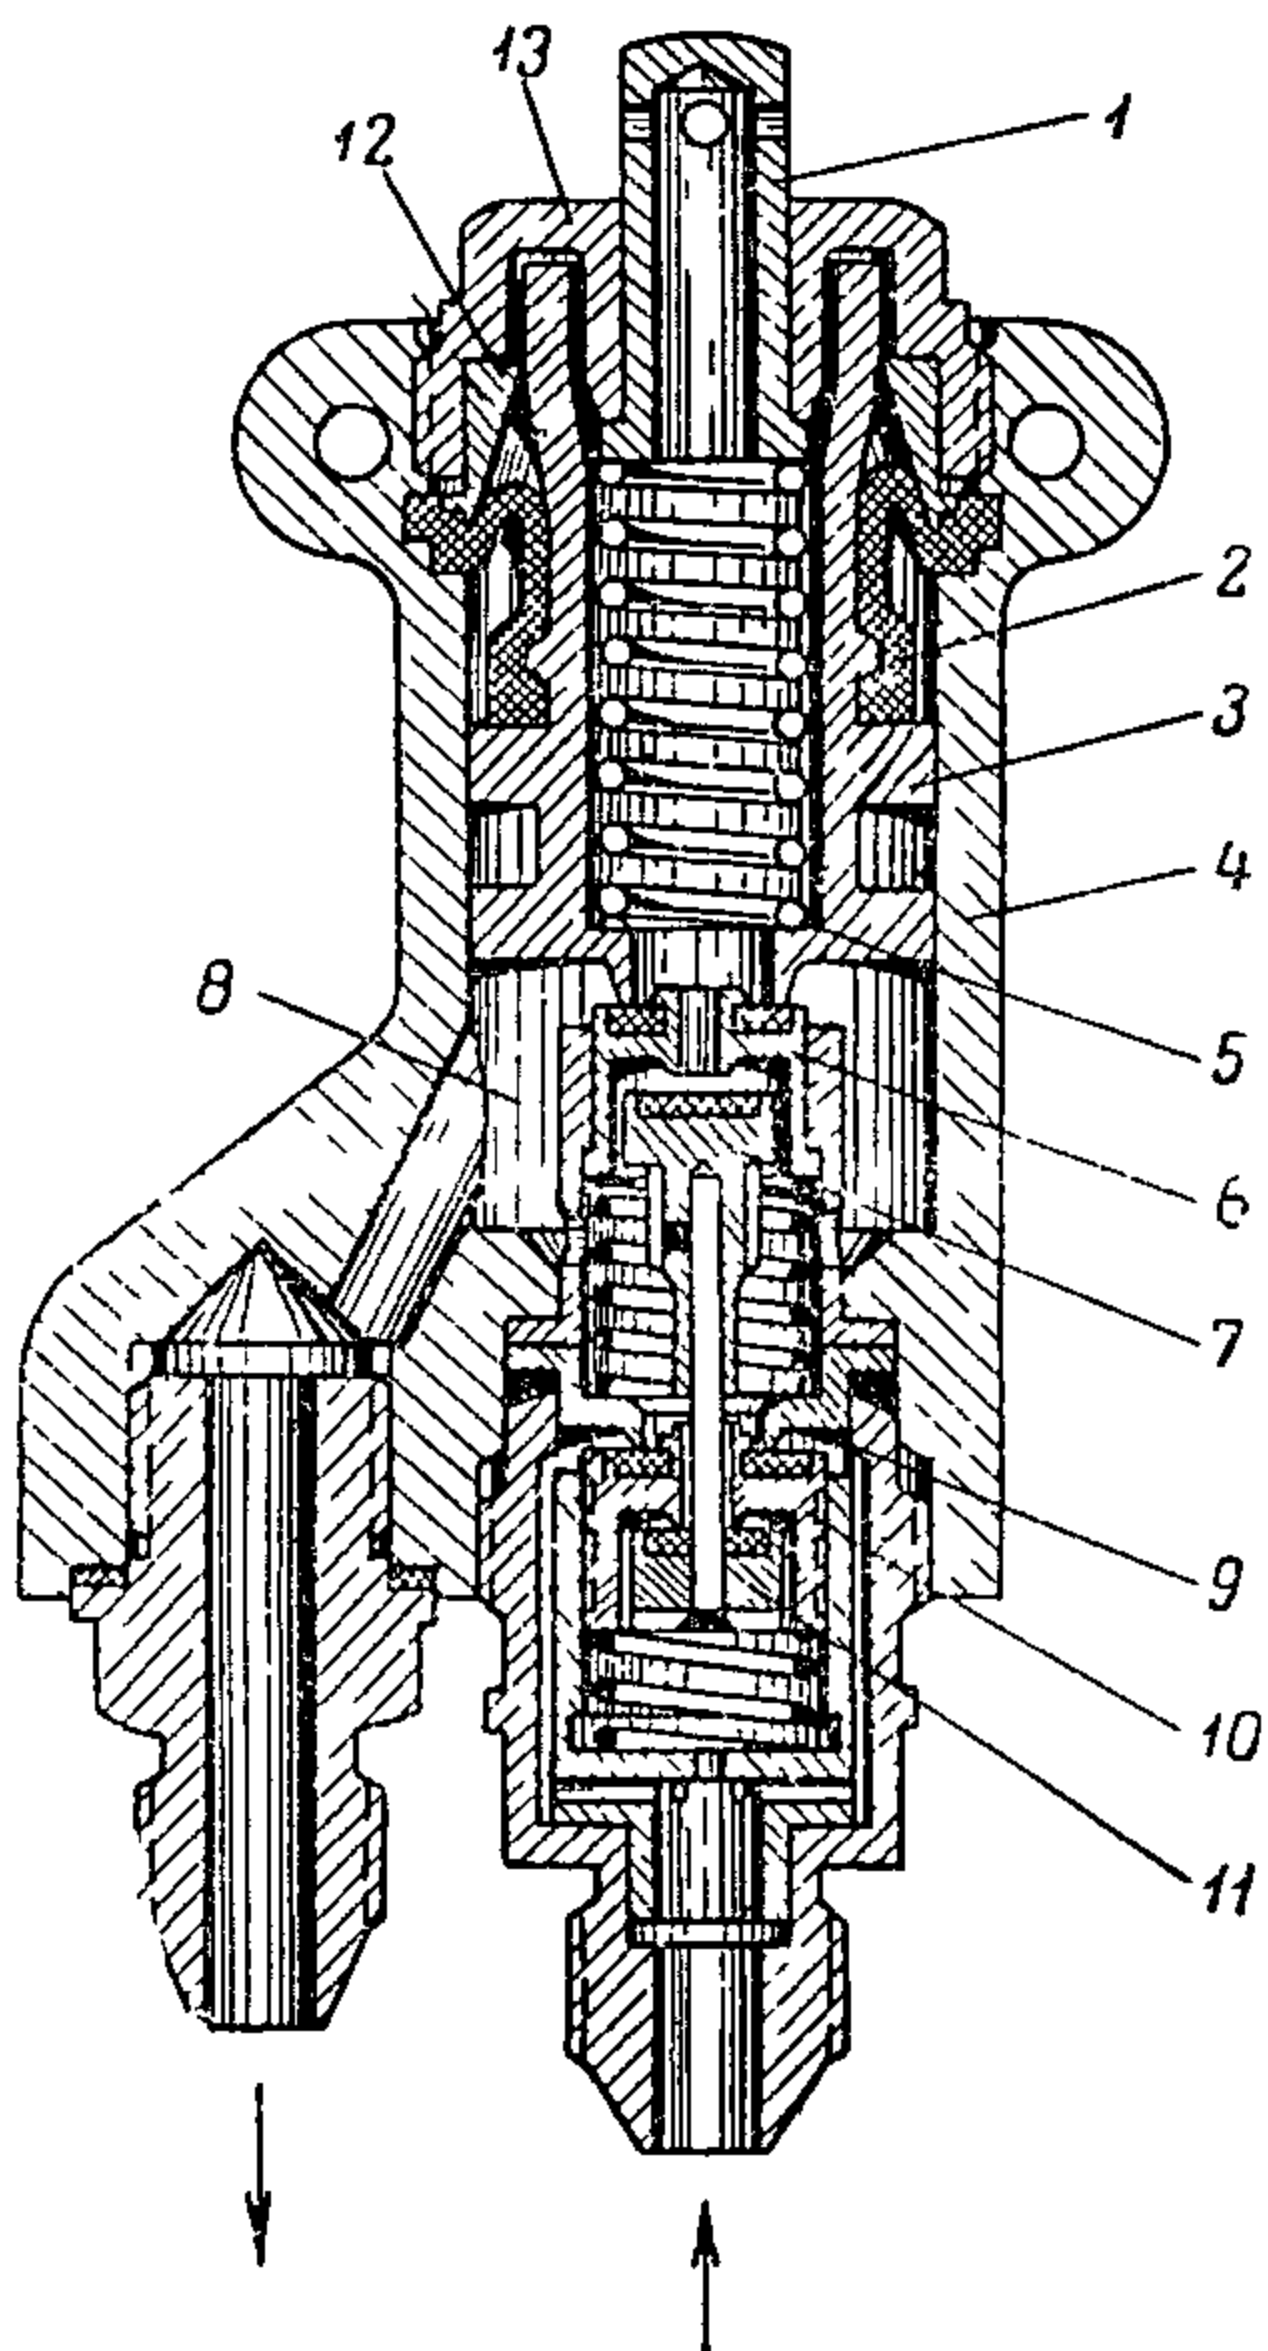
Редукционный клапан VI-39 (ПУ-7)
